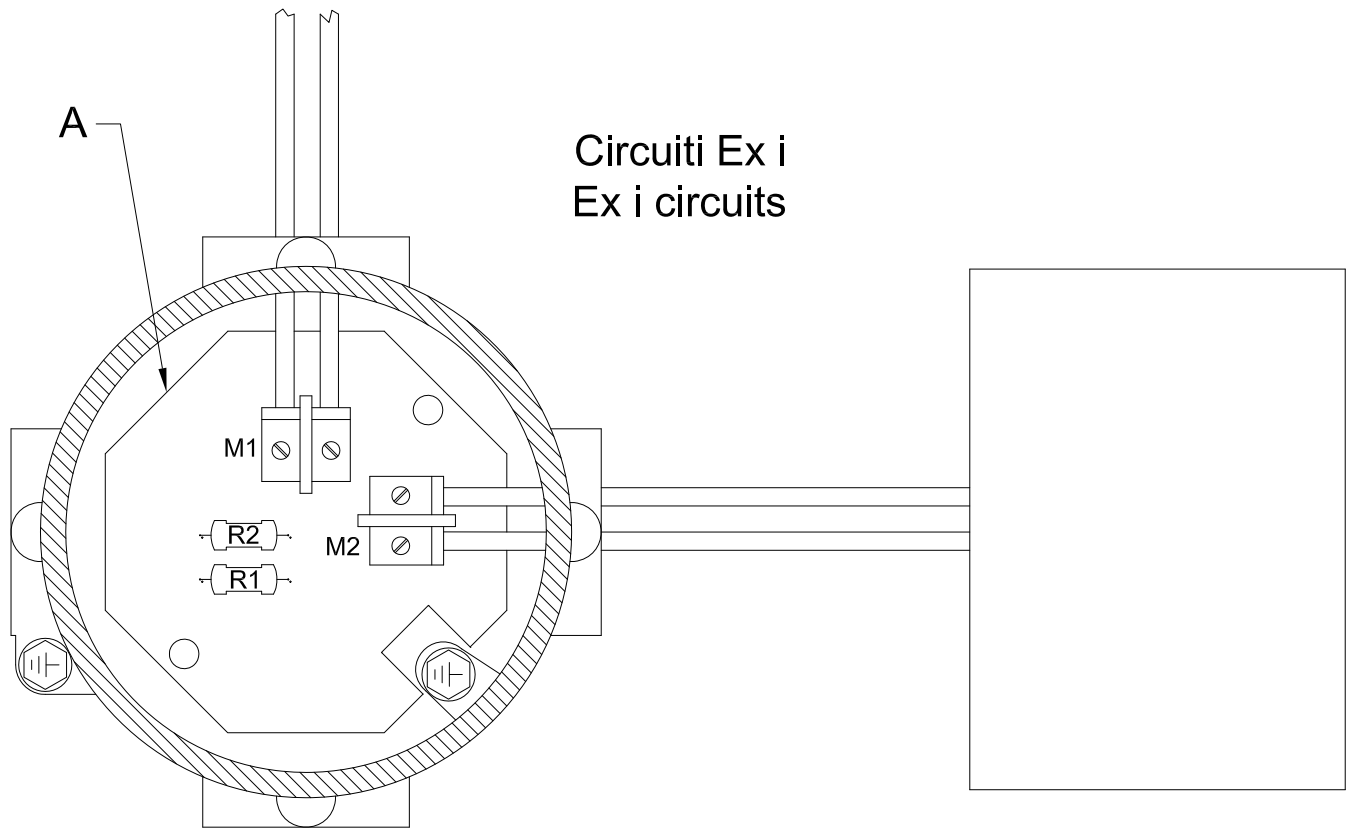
Corretto montaggio e cablaggio morsetti
